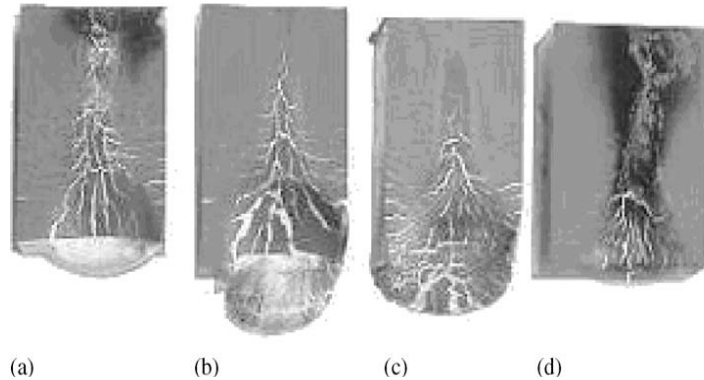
Muestras con soldadura hecha empleando ESC [11]
